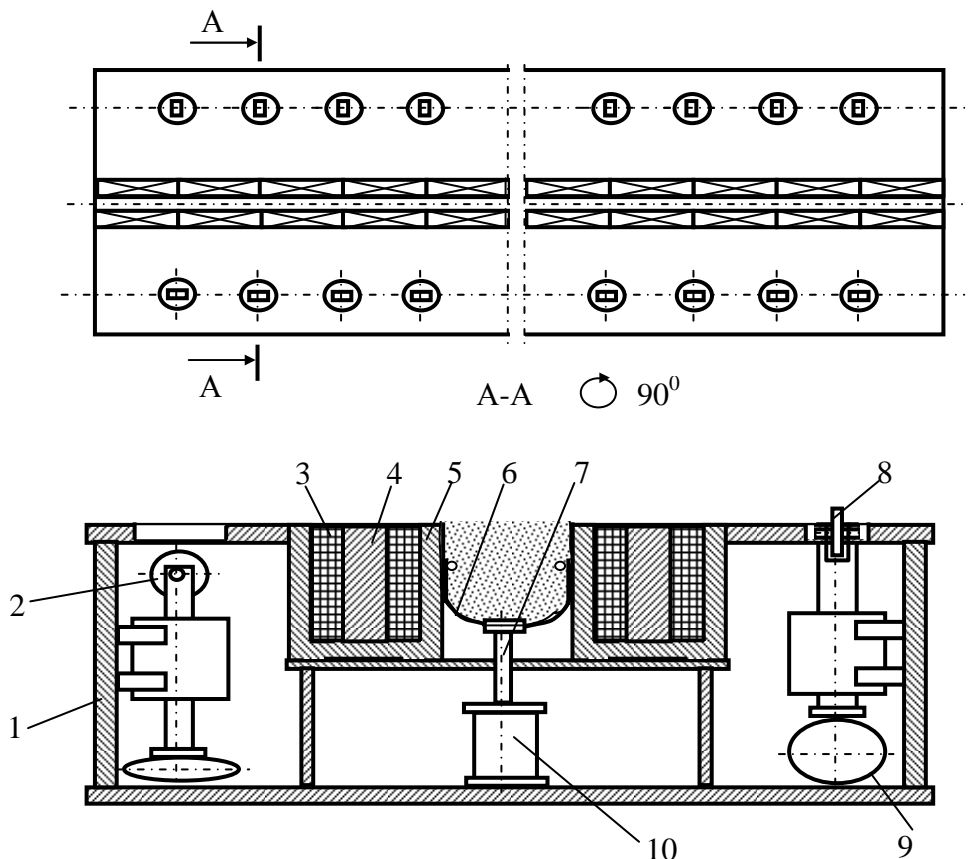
Схема електромагнітного стенда: 1-рама; 2, 8-ролики; 3-катушка; 4-осердя; 5-корпус; 6-жолоб; 7- шток; 9-пневмошланг; 10- пневмоциліндр
